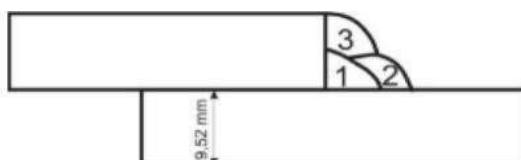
Representação da sequência de soldagem. Fonte: O autor.
